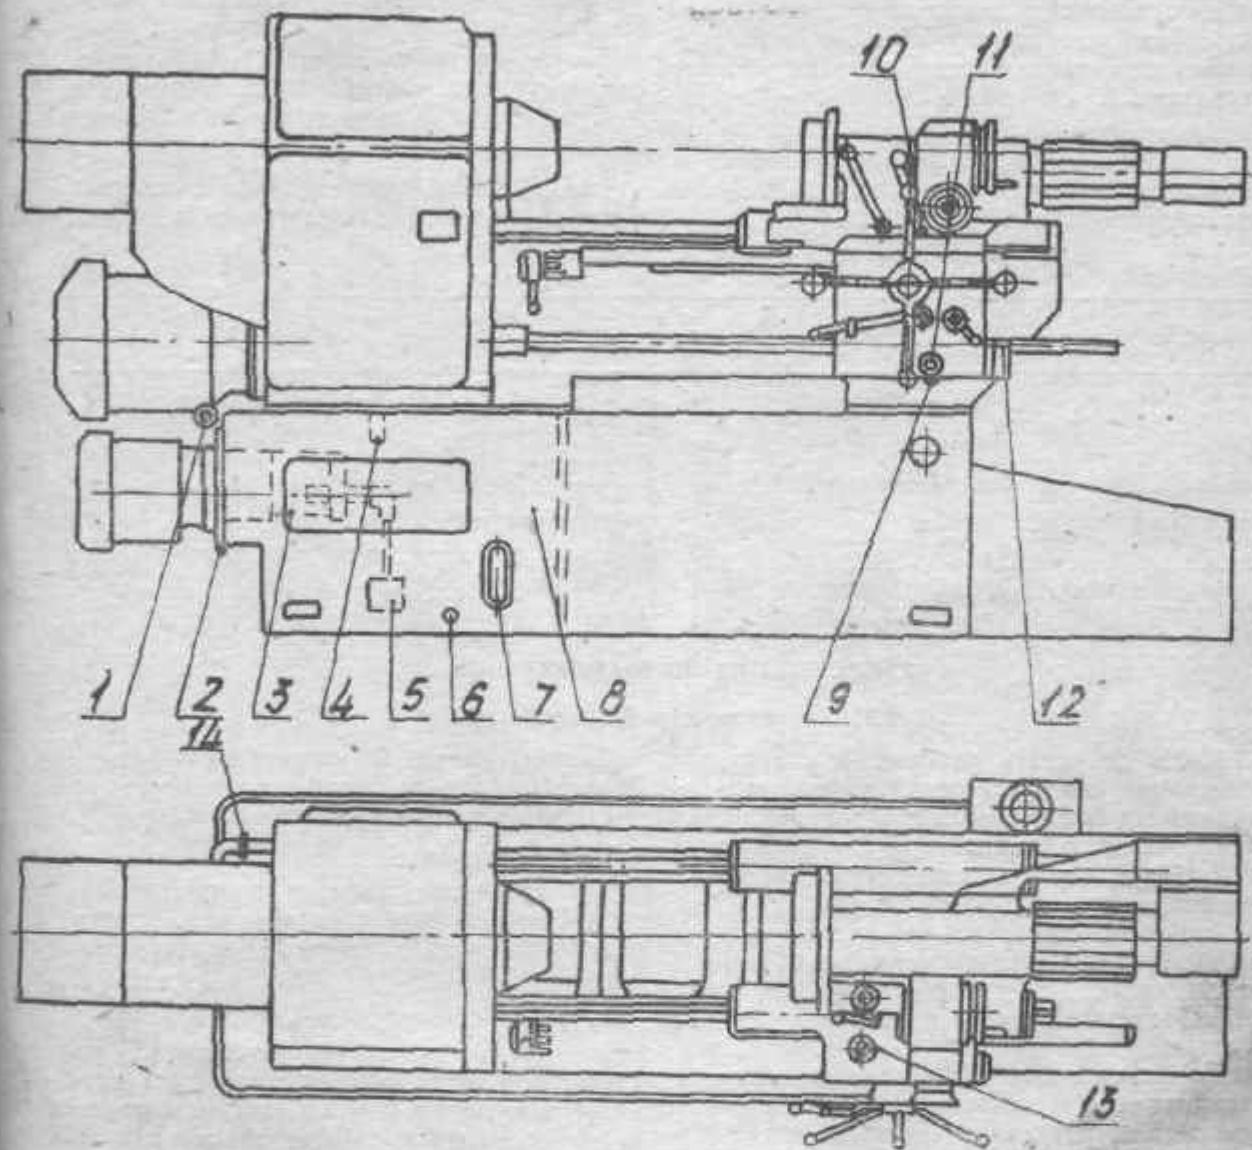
Схема расположения смазываемых и смазочных устройств станка.
